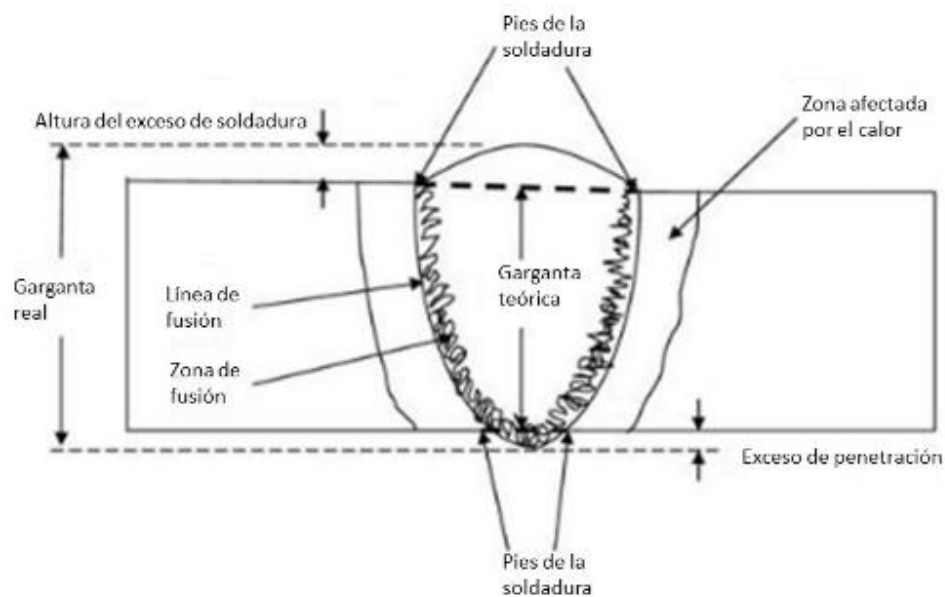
19 Componentes de una unión soldada (12)
